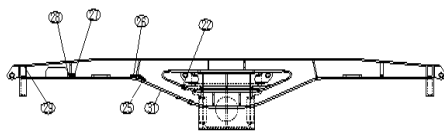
Side frame 옆면의 Strain gauge 취부도
